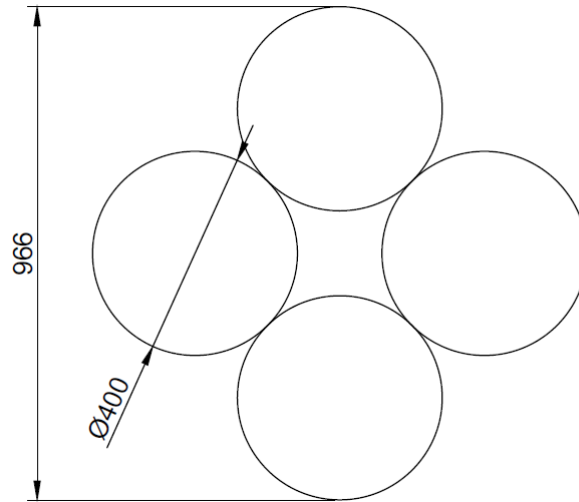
Geometría arreglo de pulverizadores en la base del cono desarrollado.
